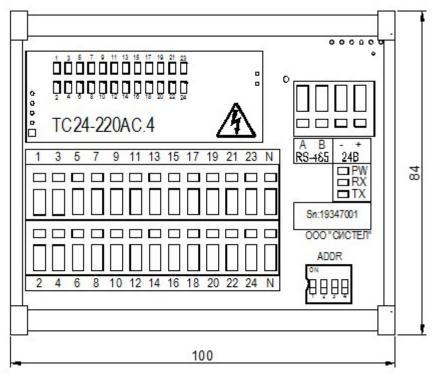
Внешний вид и габаритные размеры Устройства
